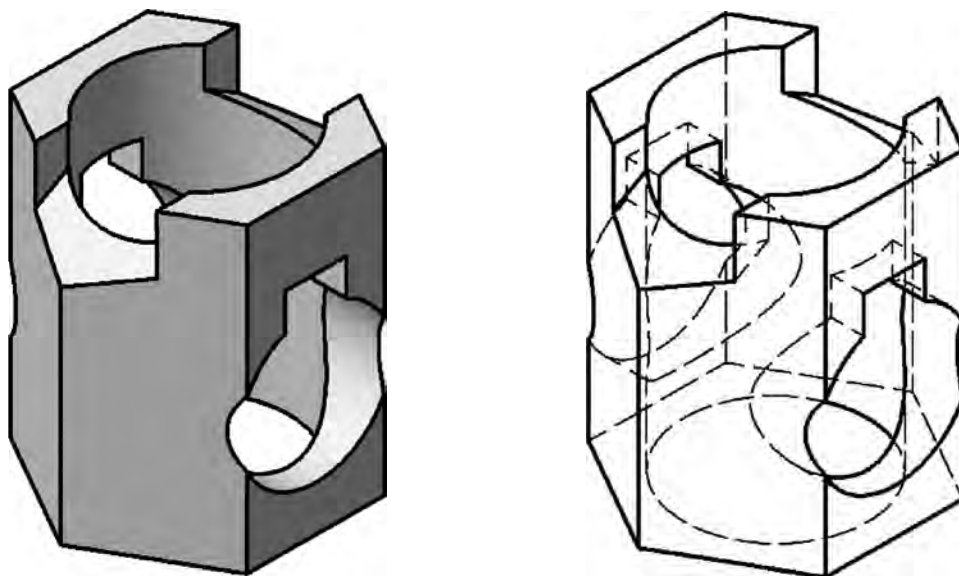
Образец призмы (к чертежу на рис. 3.4)
